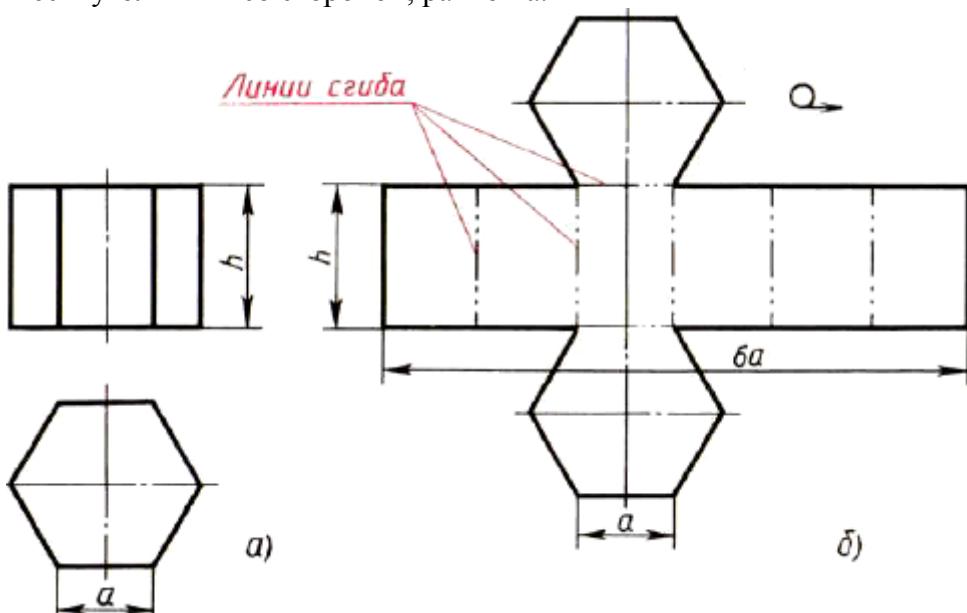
Построение чертежа развёртки поверхностей призмы: а — два вида; б — развёртка поверхностей
